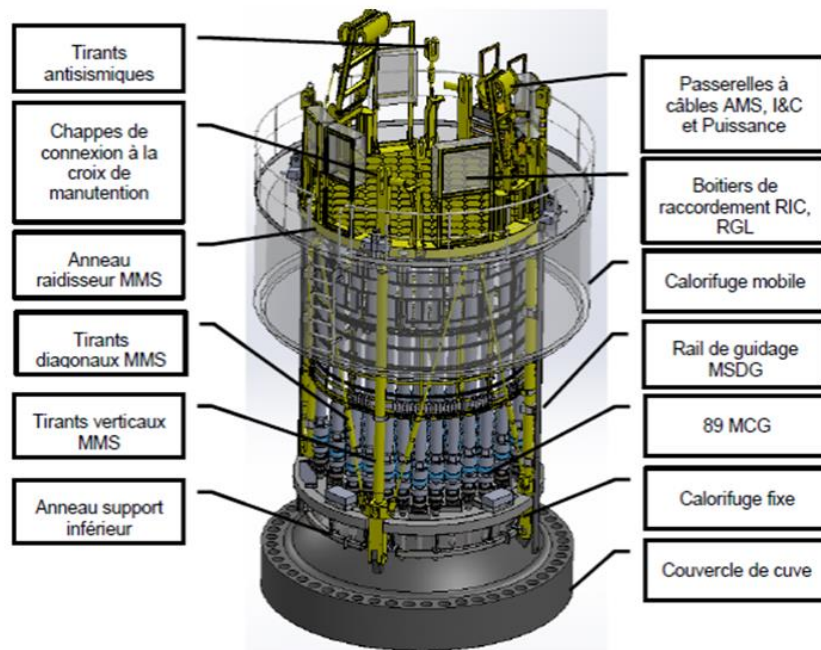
Vue d'ensemble du couvercle de la cuve.
